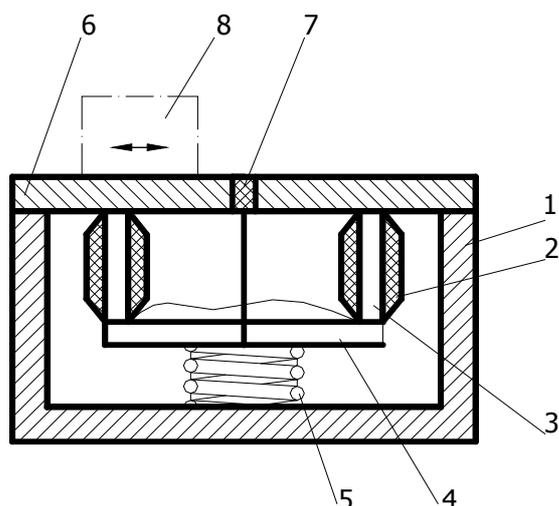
Схема работы демагнитизатора: 1 – корпус из немагнитного металла; 2 – катушки; 3 – сердечники; 4 – соединительная стальная планка; 5 – пружина; 6 – крышка; 7 – текстолитовая прокладка; 8 – деталь.
